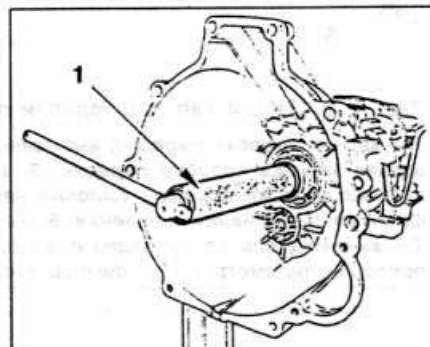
Снятие передней крышки коробки передач, образующей одно целое с направляющей втулкой подшипника выключения сцепления:
